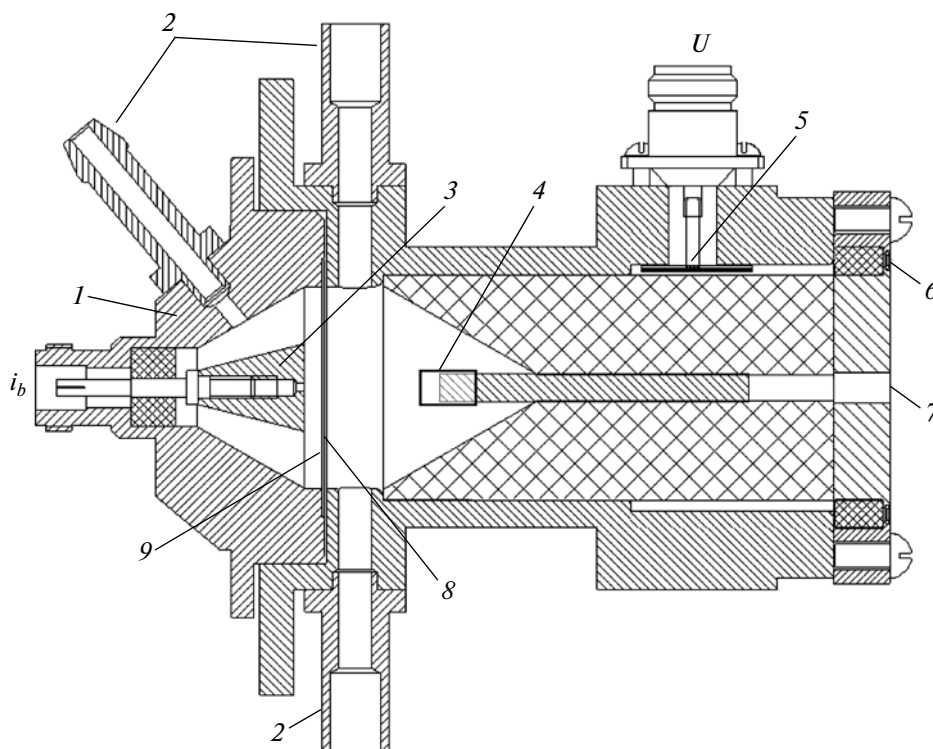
Сборочный чертеж разрядной камеры. 1 – корпус коллектора, 2 – патрубки для напуска и откачка газа, 3 – приемная часть коллектора, 4 – трубчатый катод, 5 – емкостной делитель напряжения, 6 – шунт, 7 – отверстие для подключения высоковольтного кабеля, 8 – анод из фольги или сетки.
